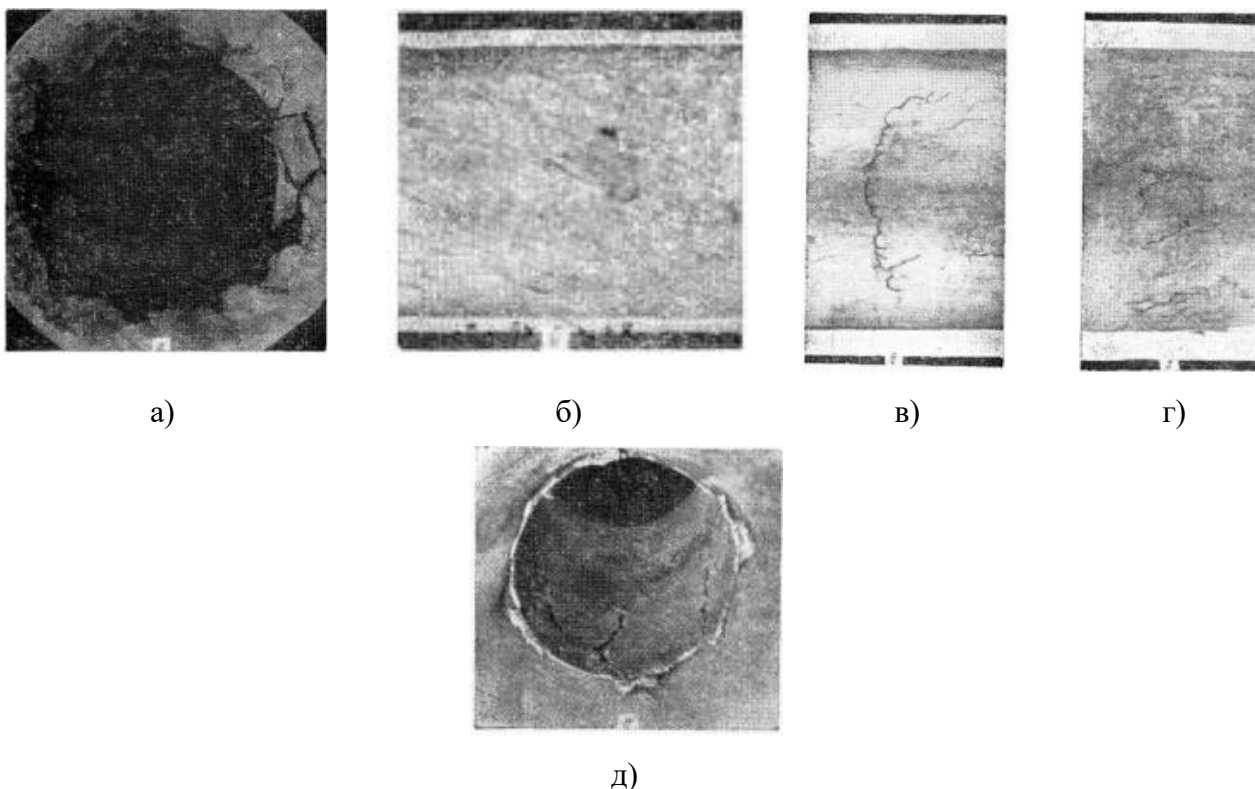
Разрушение гильз и дефекты на внутренней поверхности труб (сталь 12Х18Н10Т по ГОСТ 5632–72 [7]), вызванные перегревом металла (а), нестабильностью вторичного захвата (б), центровкой заготовки (в, г), повышенной овализацией при прошивке заднего конца заготовки (д) [36]
